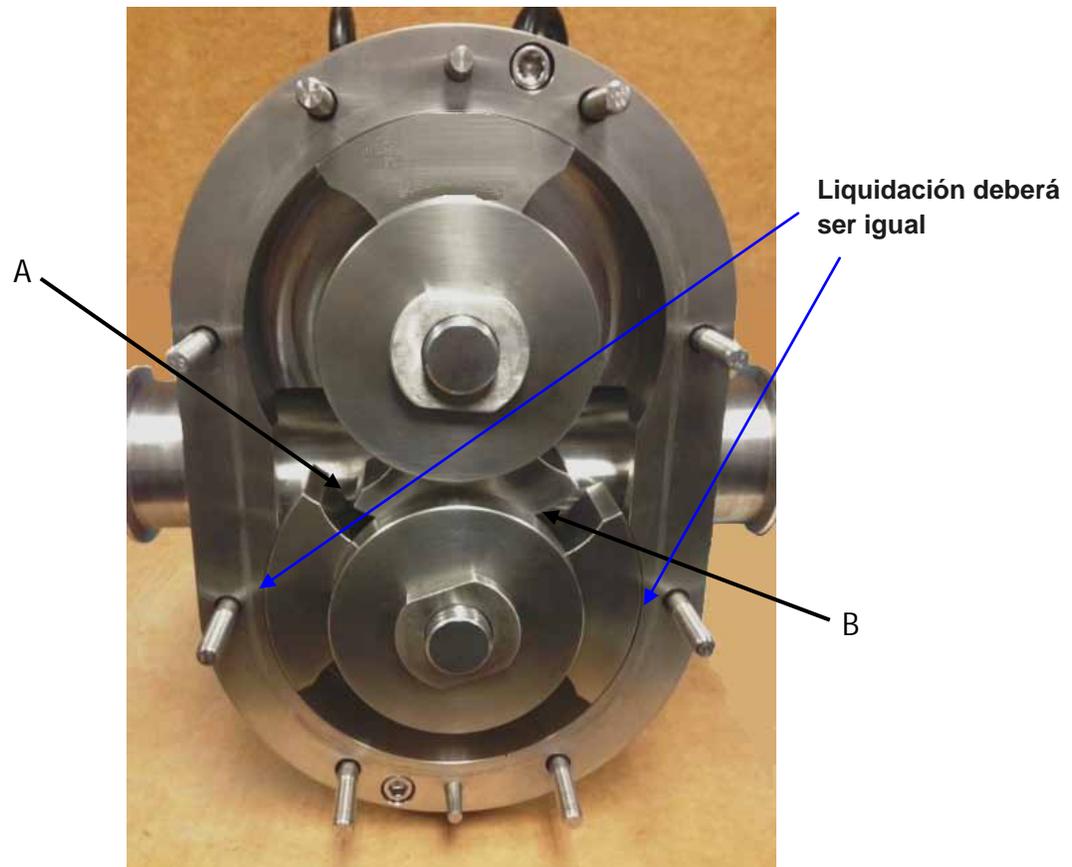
Rotor a Rotor Tip Tolerancias
